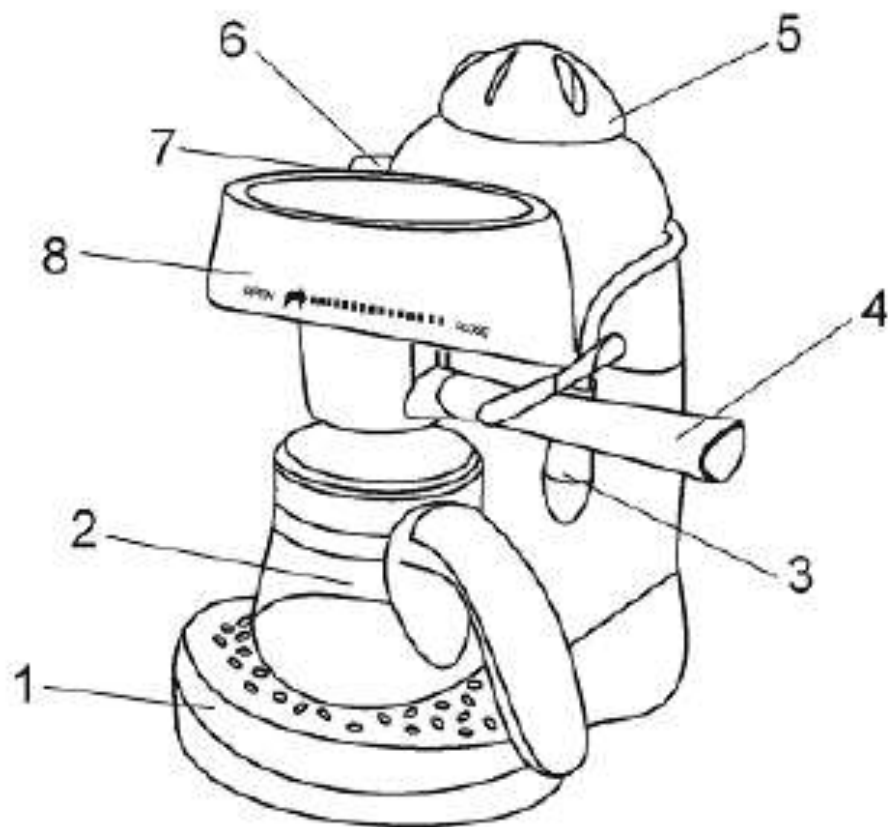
Загальний вигляд кавоварки Scarlett SC-037
